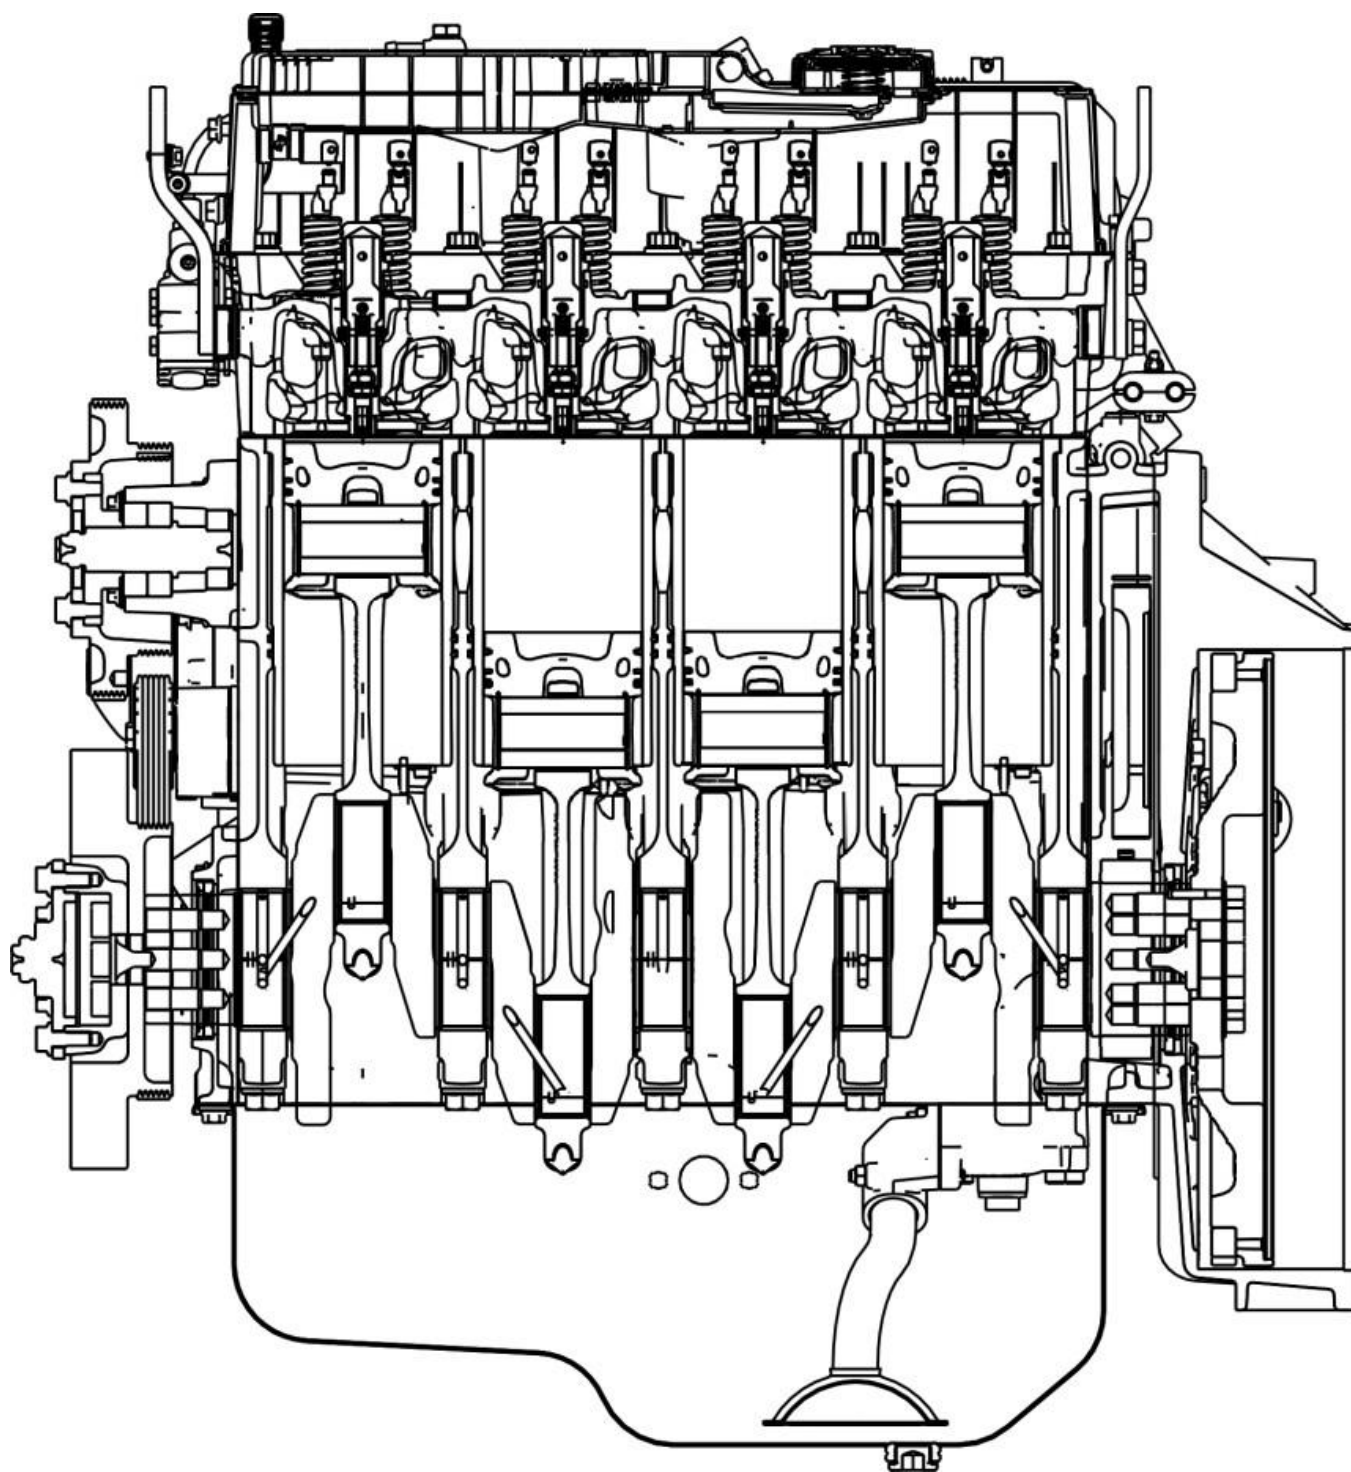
Продольный разрез двигателя ЯМЗ-53414
